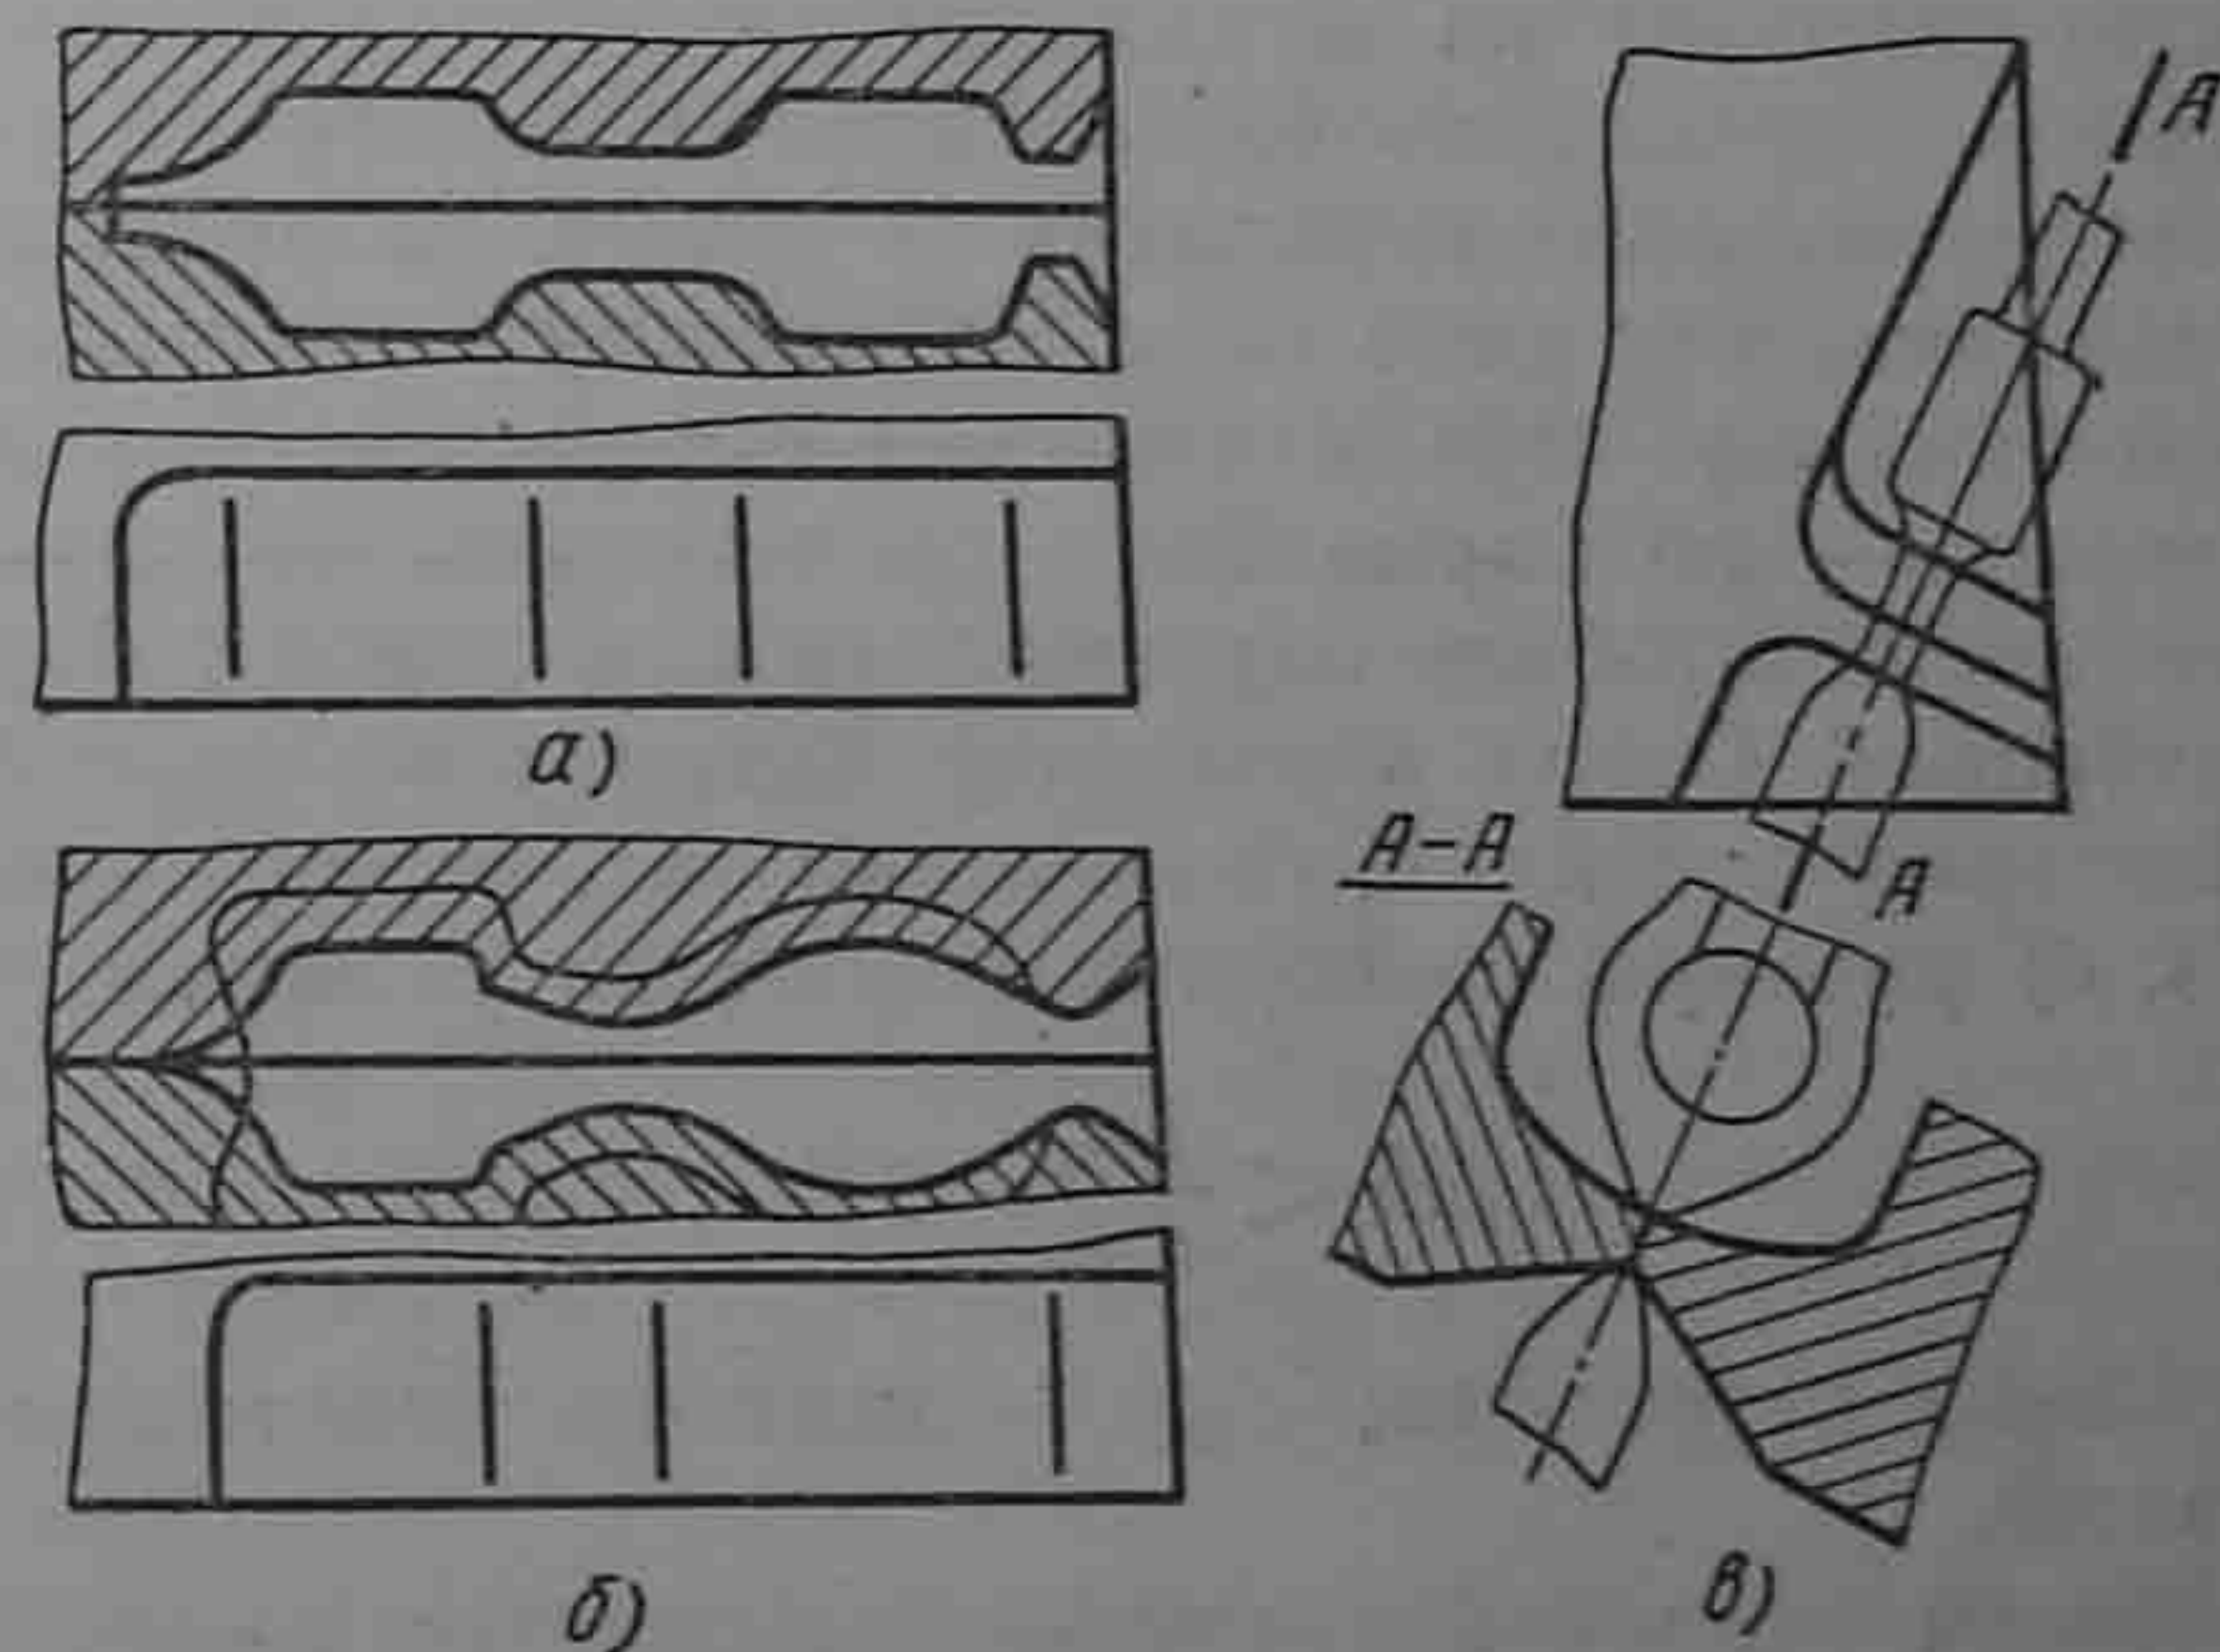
Пережимной (а), формовочный (б) и отрубной (в) ручьи
